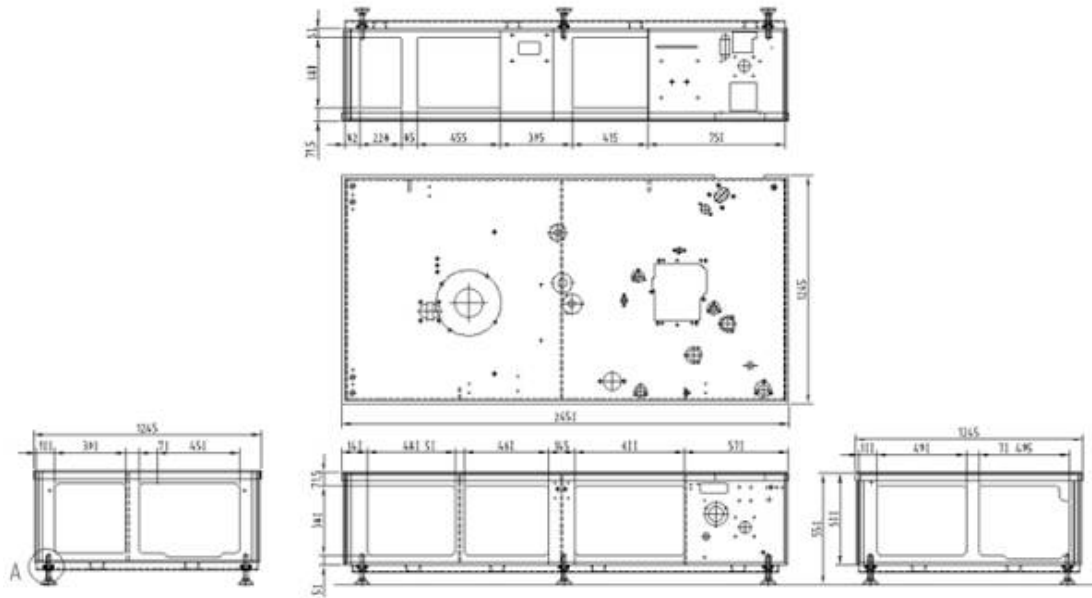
Auto Packaging M/C Main Frame의 2D 설계도면
